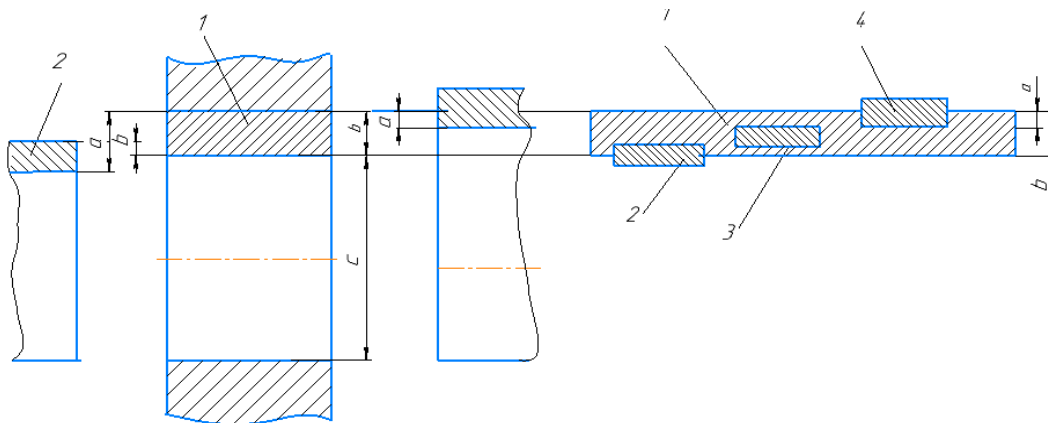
Графическое представление переходной посадки. 1- интервал допуска отверстия; 2–4 – интервал допуска вала (показано несколько возможных расположений); a – наибольший зазор; b – наибольший натяг; c – номинальный размер, равный нижнему предельному размеру отверстия
